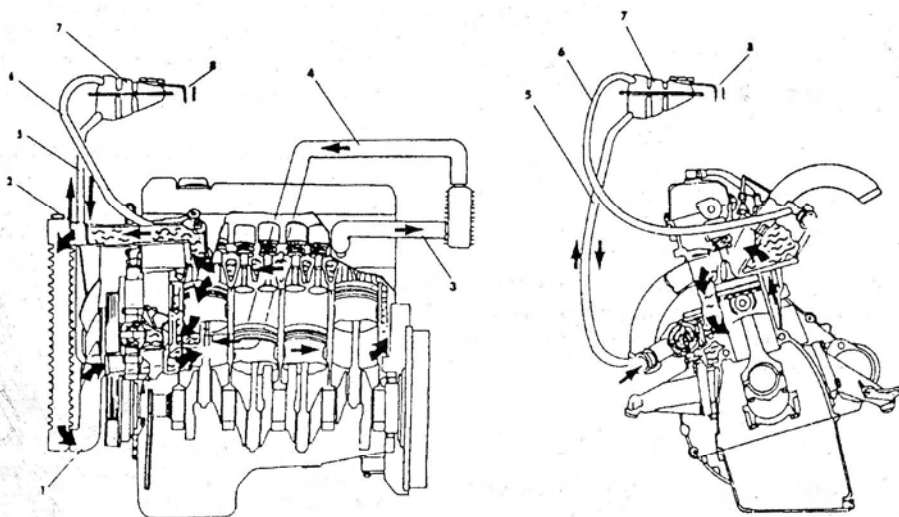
Схема системы охлаждения с расположением отдельных элементов. Показан четырехцилиндровый двигатель. Схема для пятицилиндрового двигателя отличается наличием дополнительного цилиндра.
